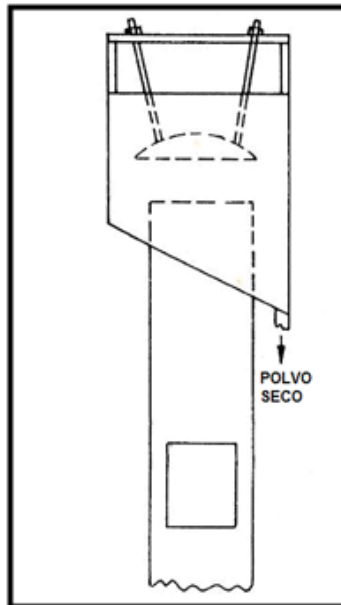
Cámara de decantación por vía húmeda del cubilote encontrado en la planta de Aceros de la Universidad Industrial de Santander.
